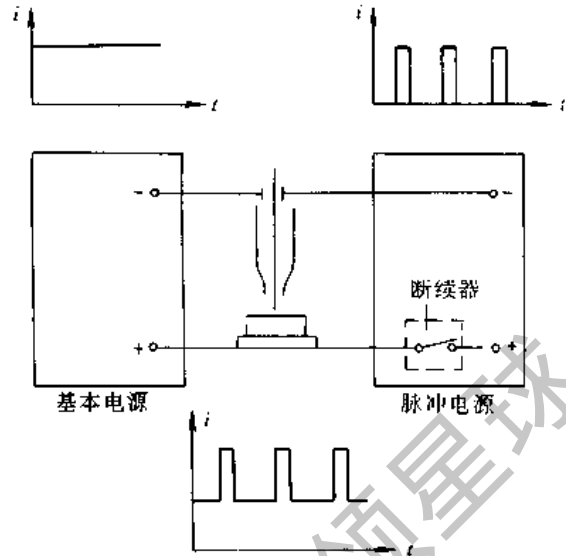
双电源供电 TIG 焊原理示意图
